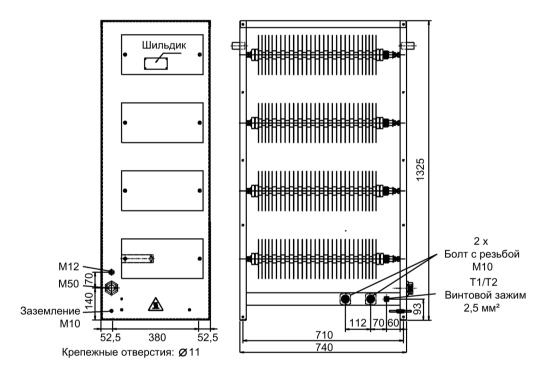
Габаритный чертеж тормозного резистора 50 кВт / 250 кВт
